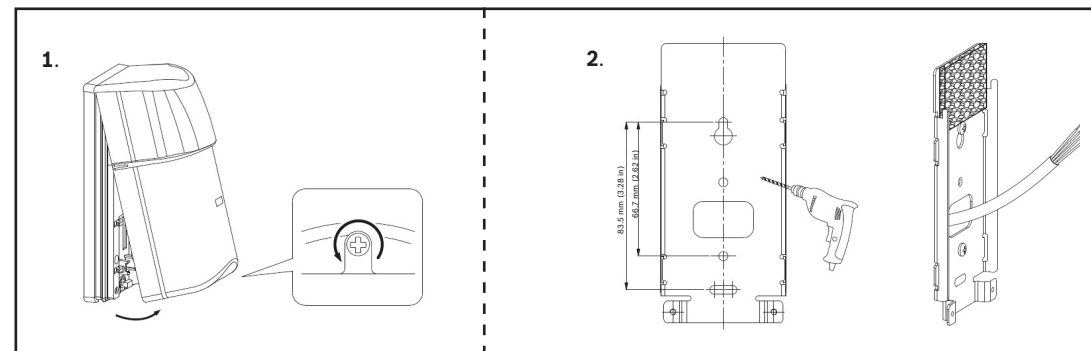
Ajuste de la placa de montaje y extracción de la cubierta
